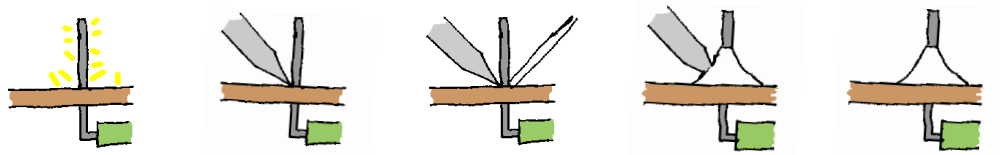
Procedimiento para soldar componentes a placas de circuito impreso
